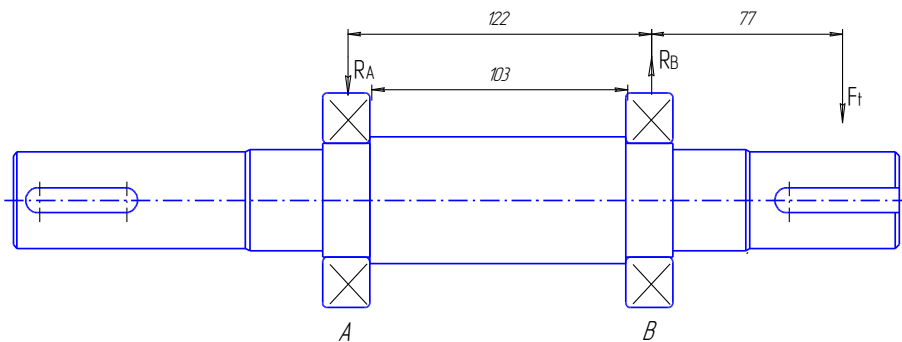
Розрахункова схема навантаження вала підшипникового вузла.
